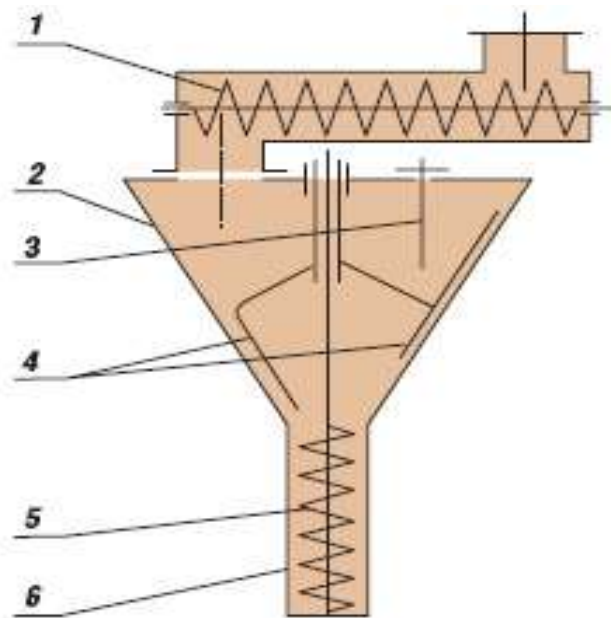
Схема шнекового дозатора: 1 - живильний шнек;
